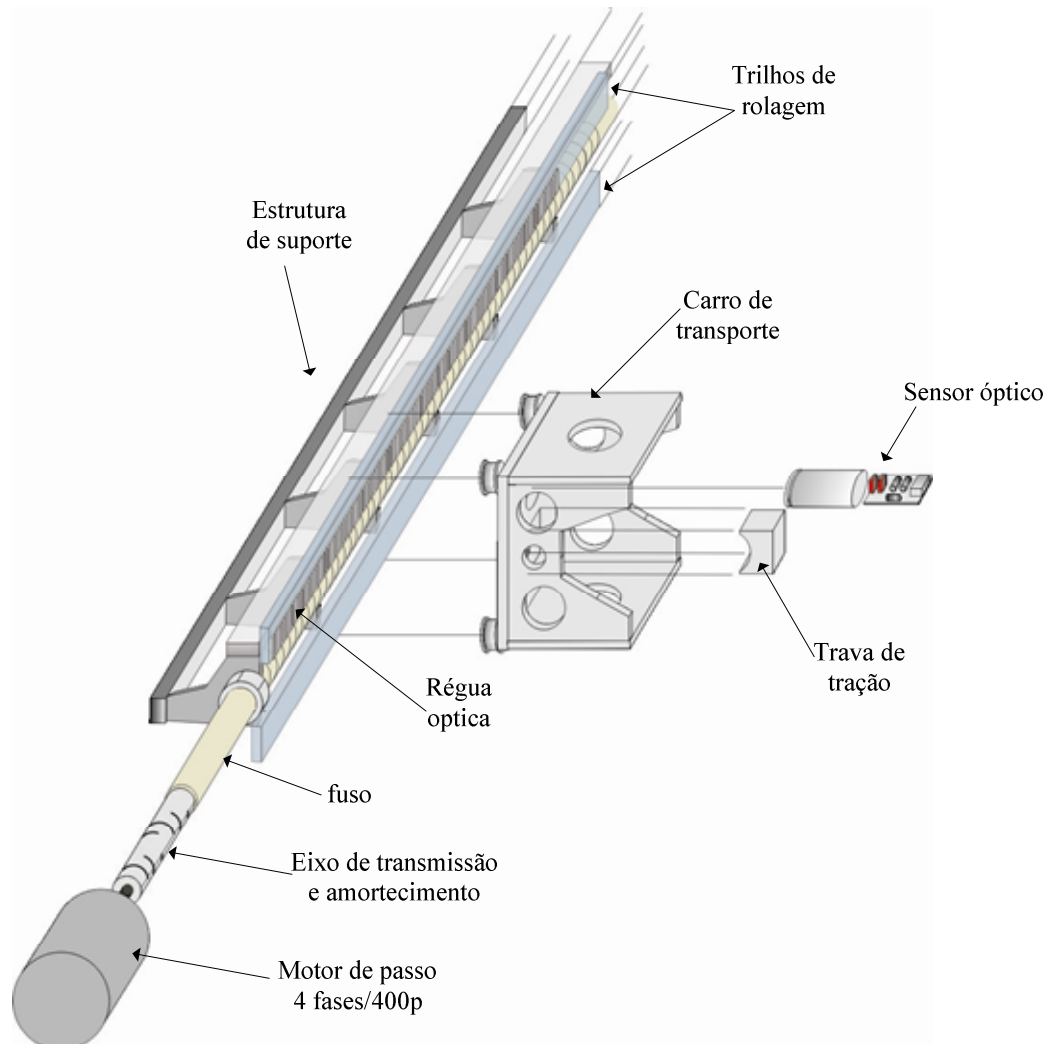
Vista parcial da estrutura de suporte e transporte do conjunto Tx-Rx, em detalhes.
